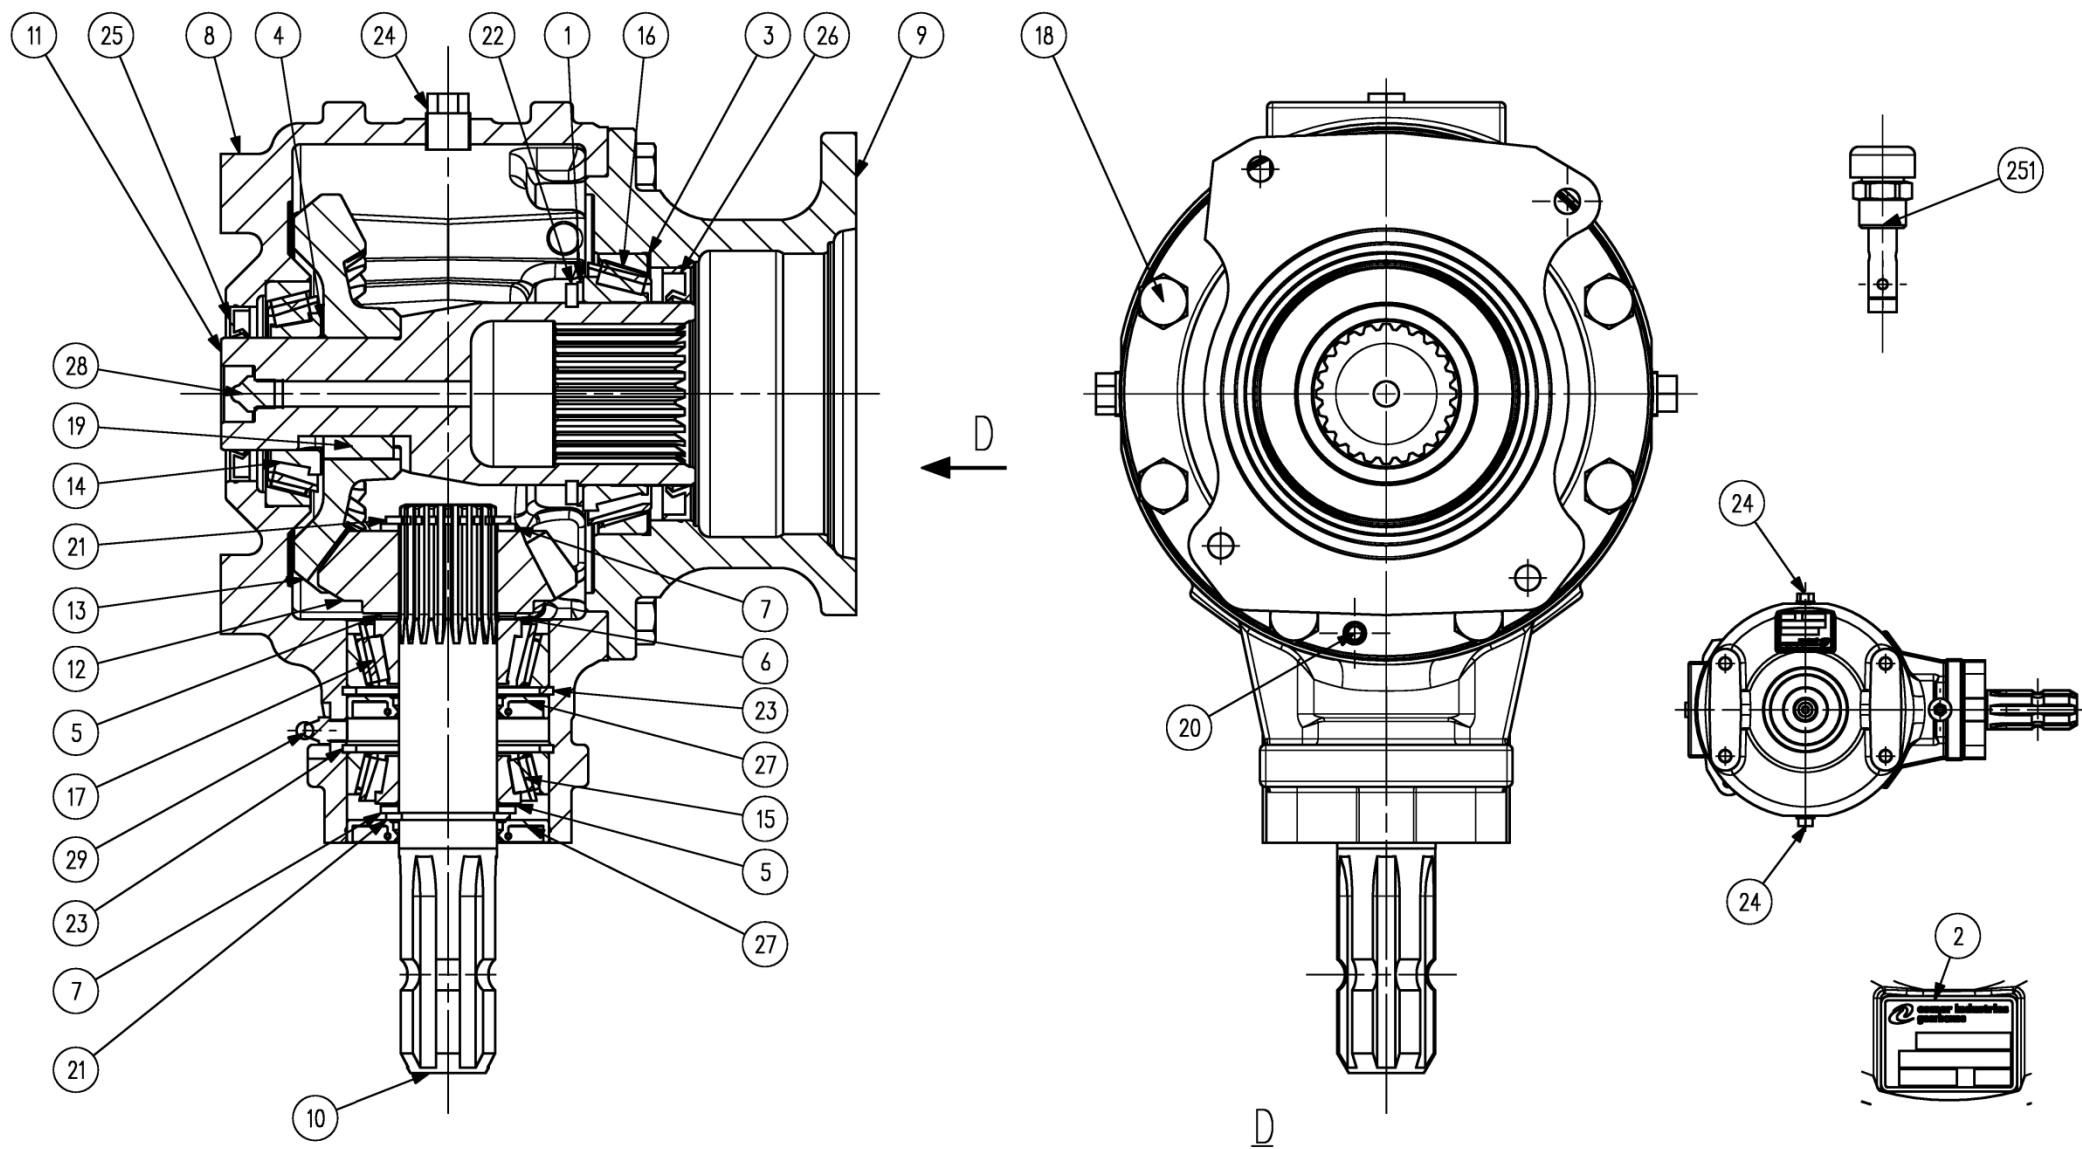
Редуктор 9.304.531.10 (9.304.531.00) "Comer industries"
